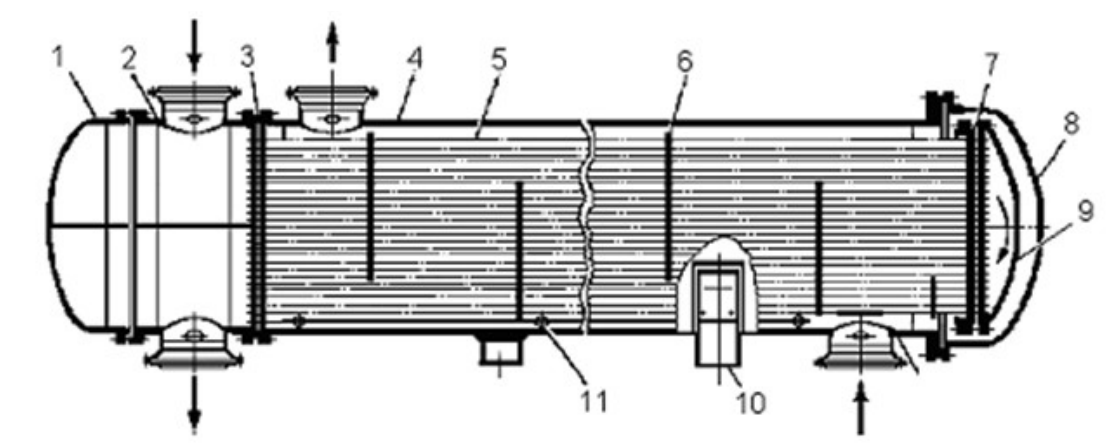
Кожухотрубчатый теплообменник с плавающей головкой
